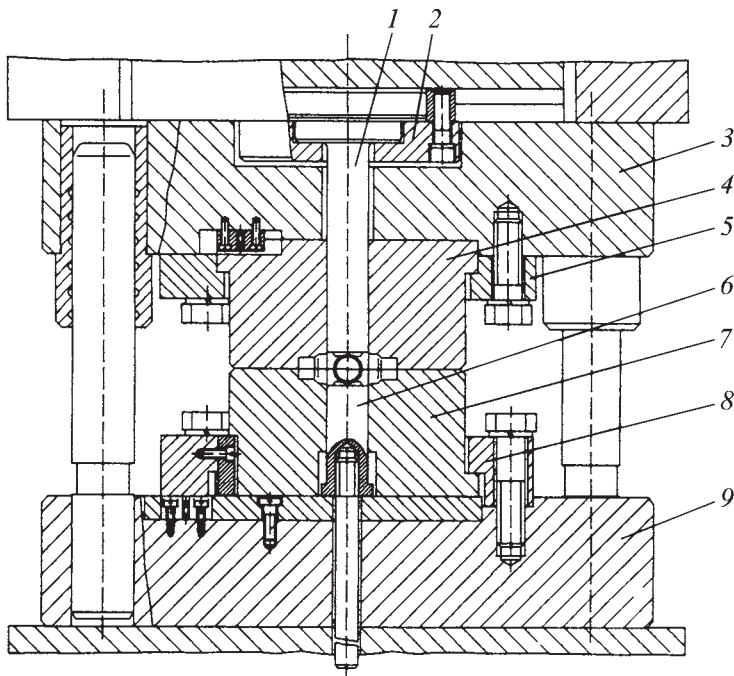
Блок штампа для штамповки в закрытых штампах с разъемными матрицами
